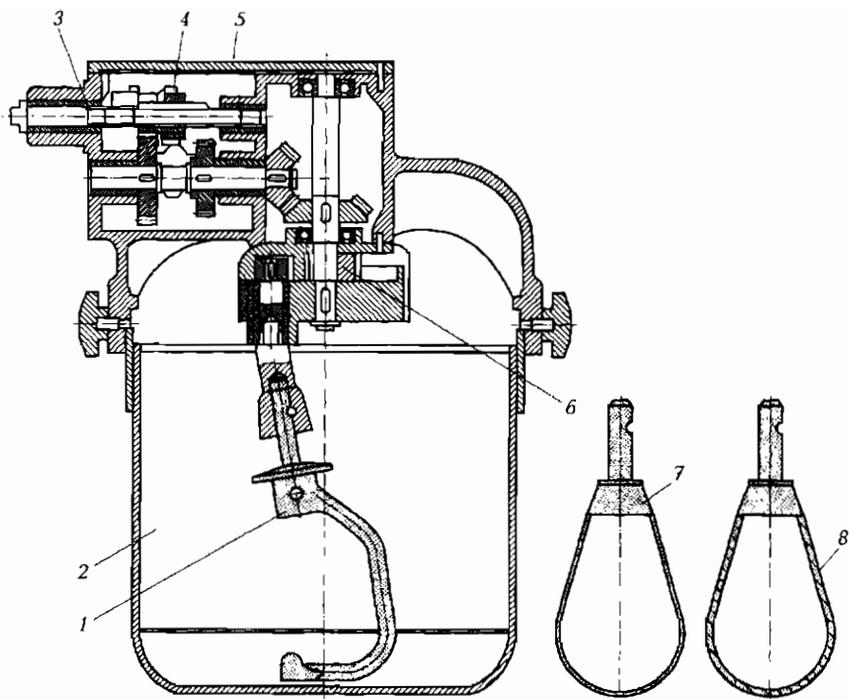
Механизм для взбивания и перемешивания МКР-25:
